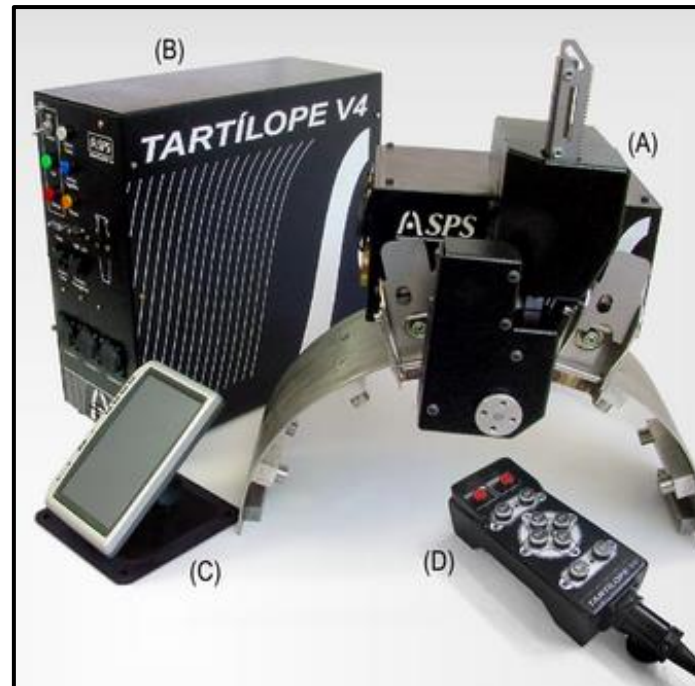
Módulos do sistema Tartílope v4: (a) manipulador da tocha de soldagem; (b) controlador; (c) interface homem-máquina e (d) controle remoto [Fonte: SPS, 2013].
